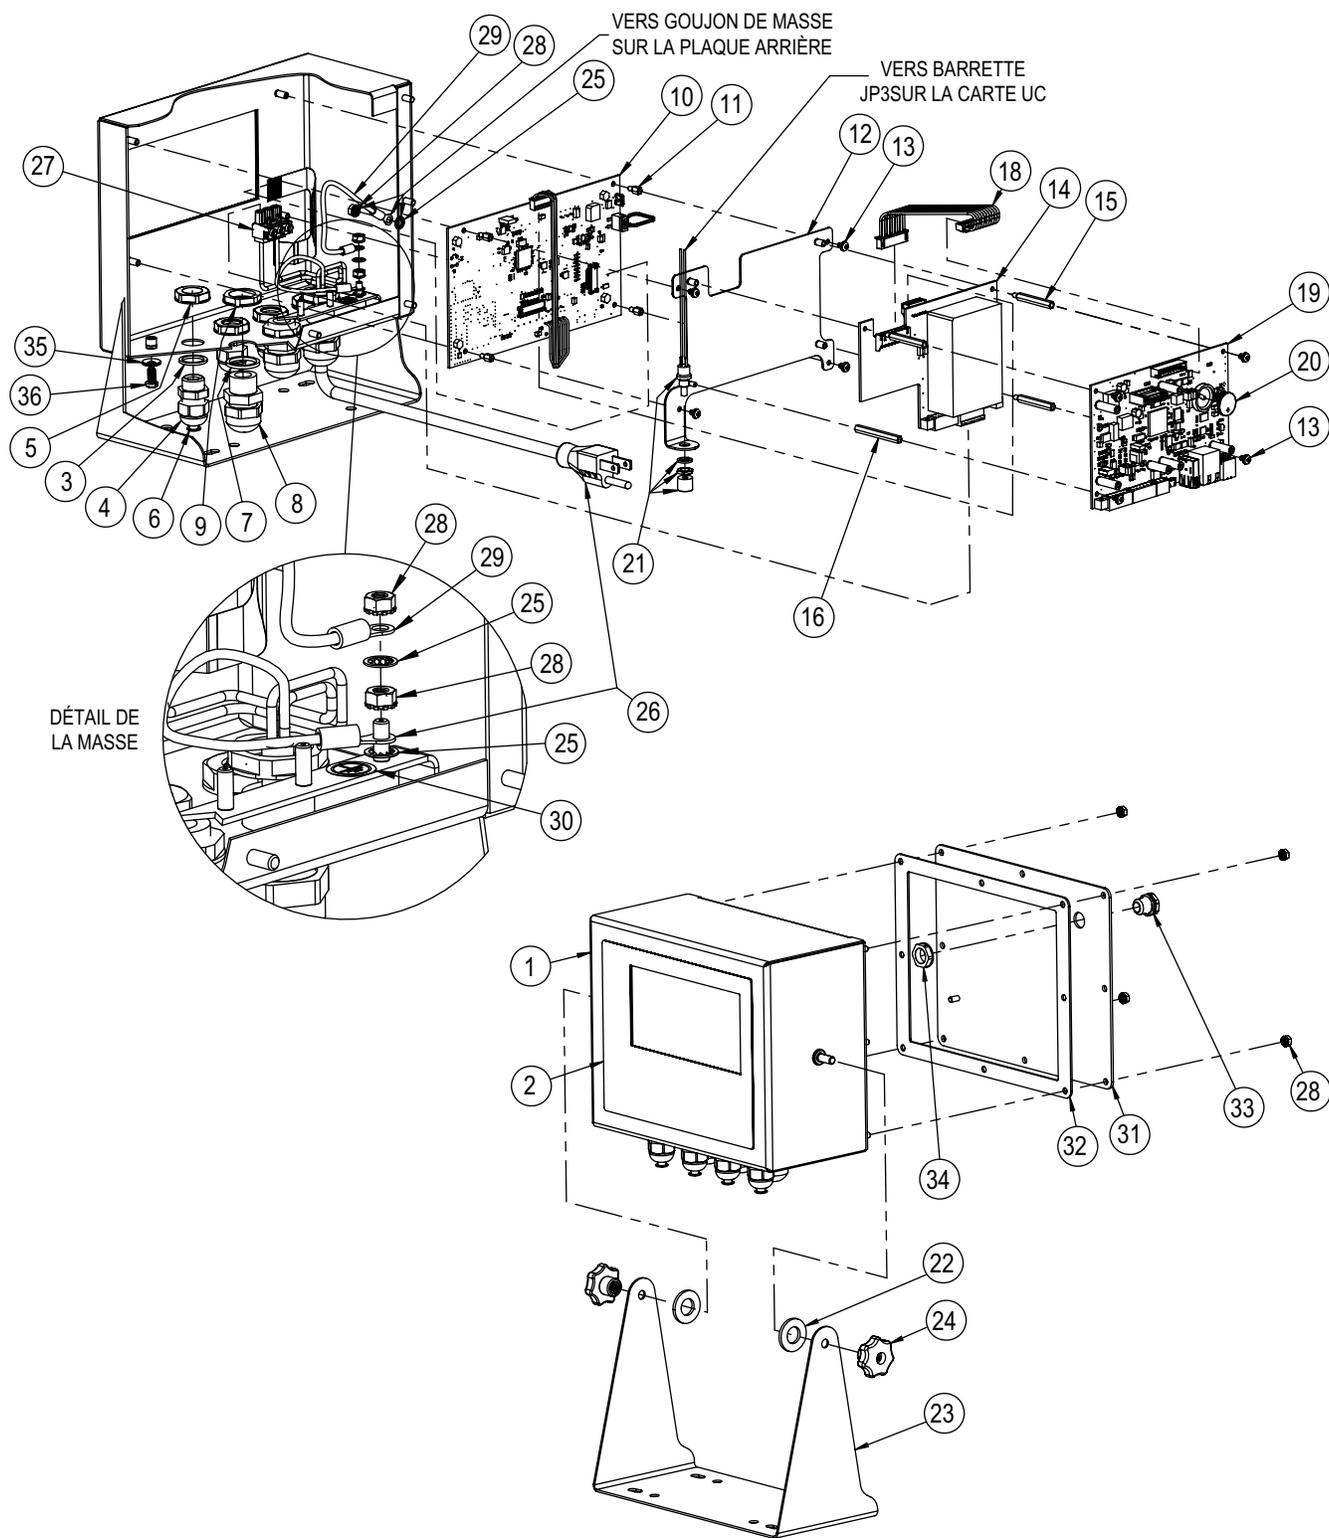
Schéma des pièces de rechange (vue éclatée)
